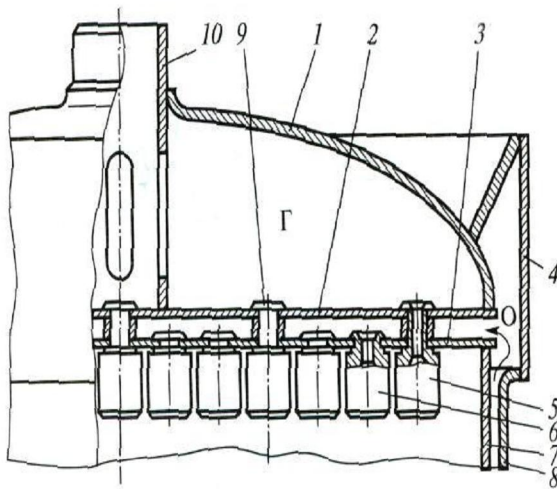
Конструкция плоской форсуночной головки ЖРД
